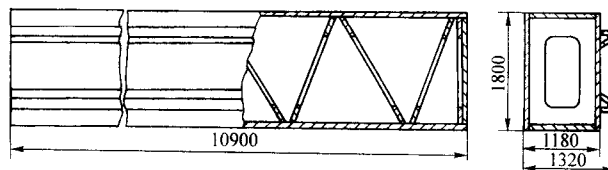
螺旋桨翼面加工专用机床焊接横梁
